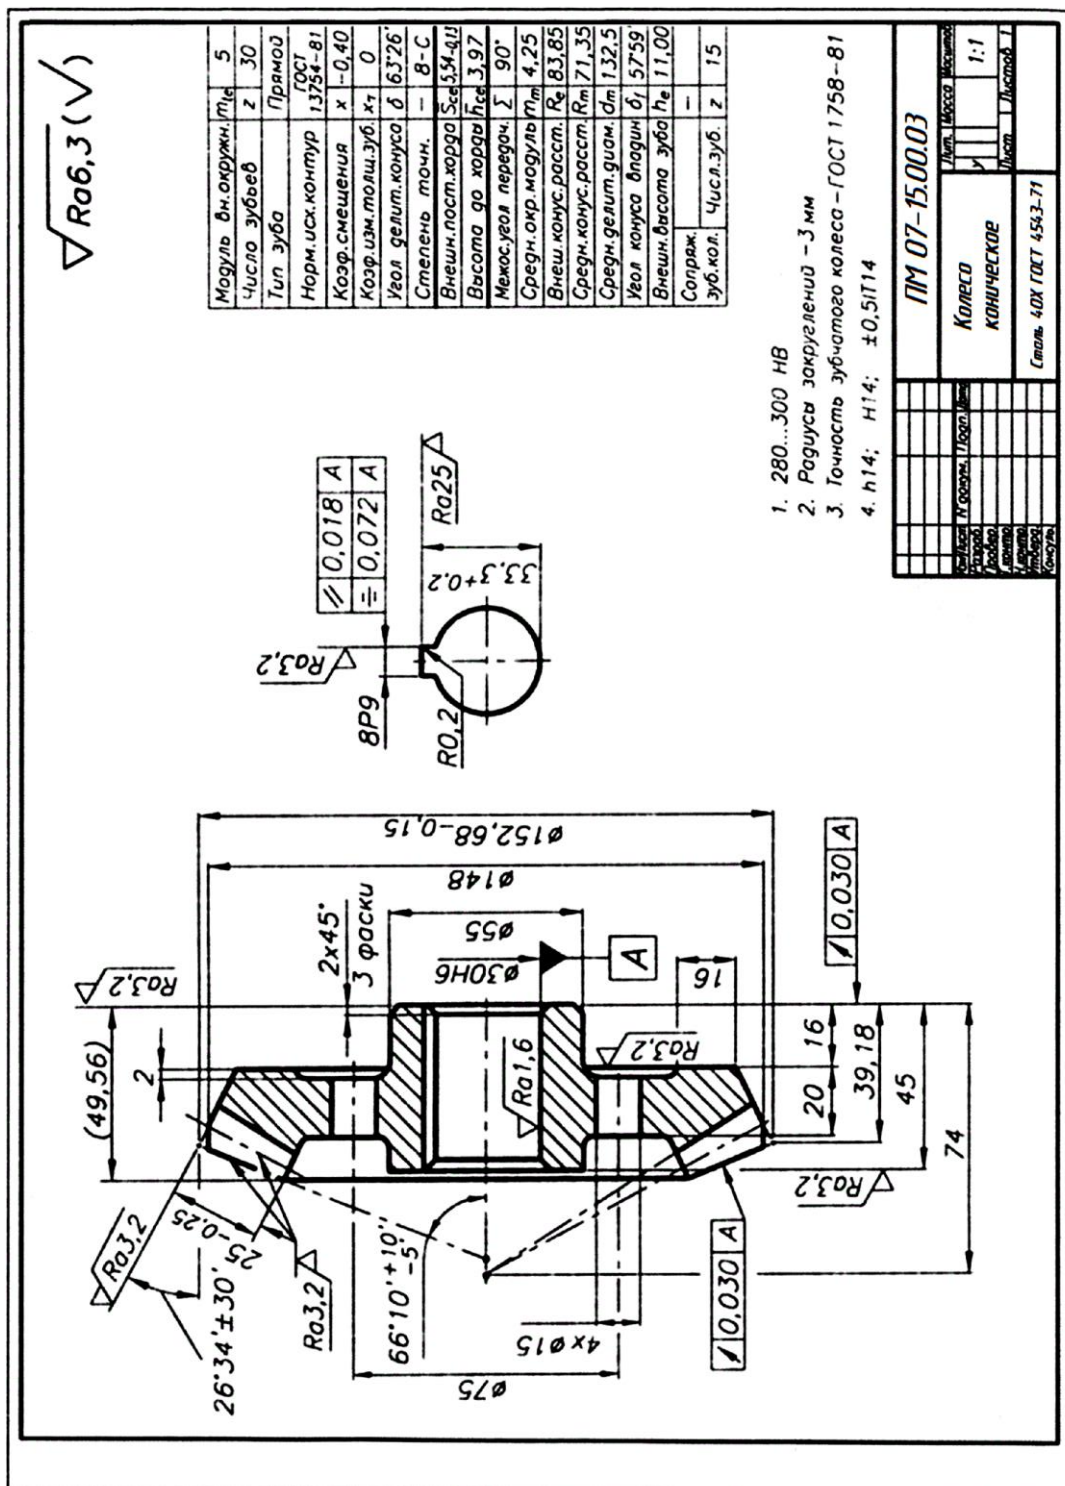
Пример рабочего чертежа конического зубчатого колеса
